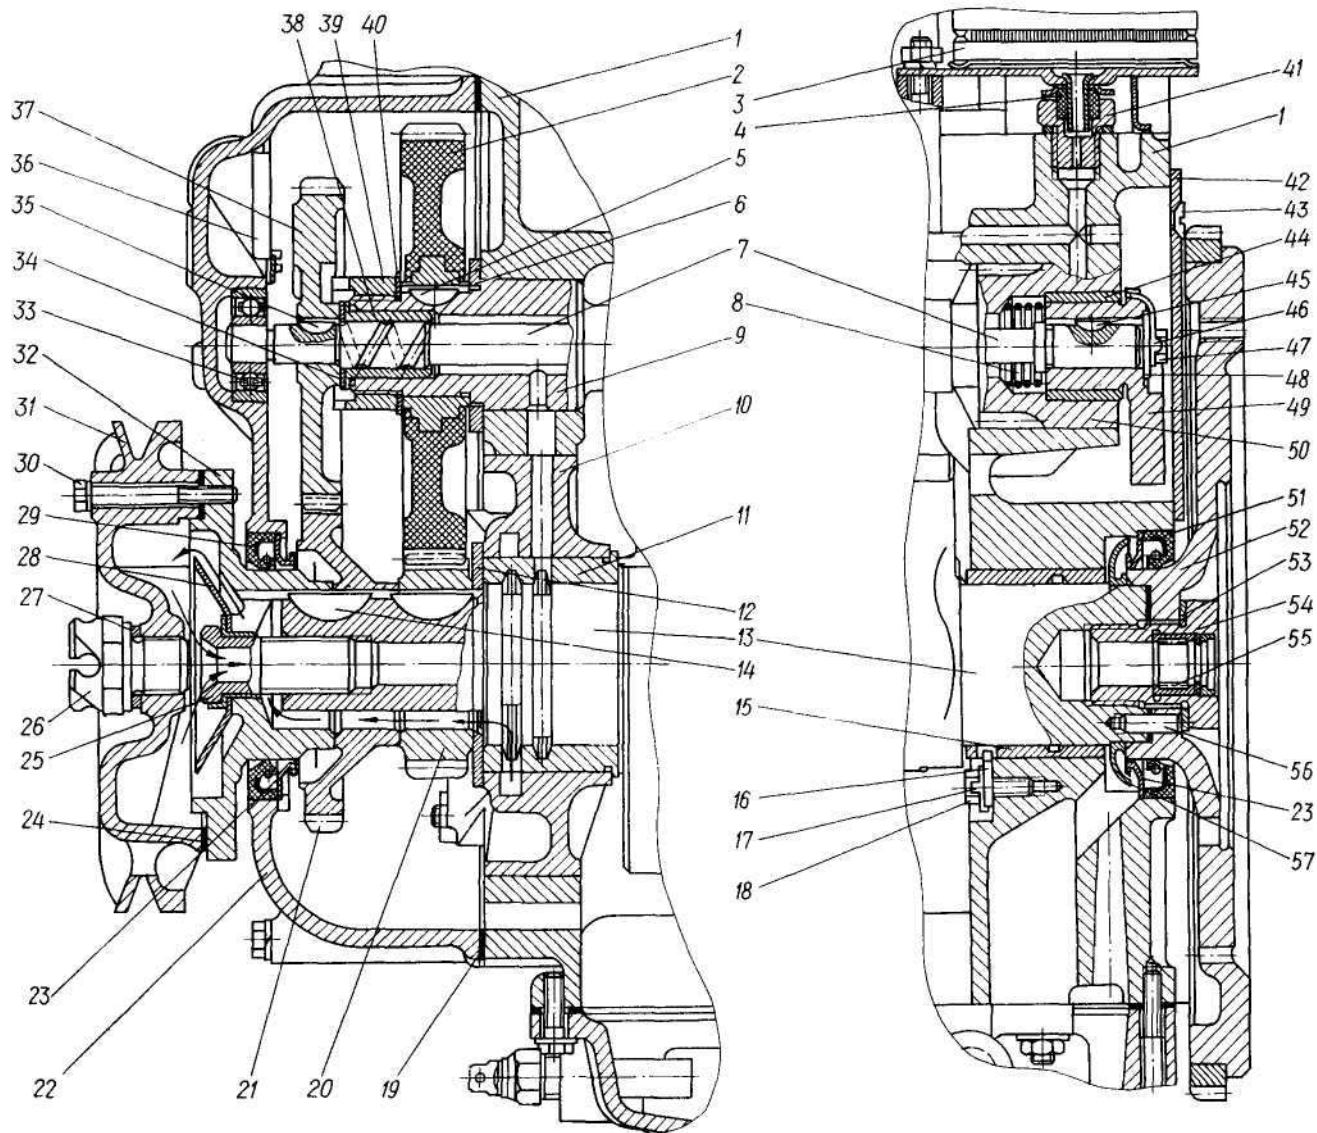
Привод распределительного вала, балансирного механизма и задний коренной подшипник:
